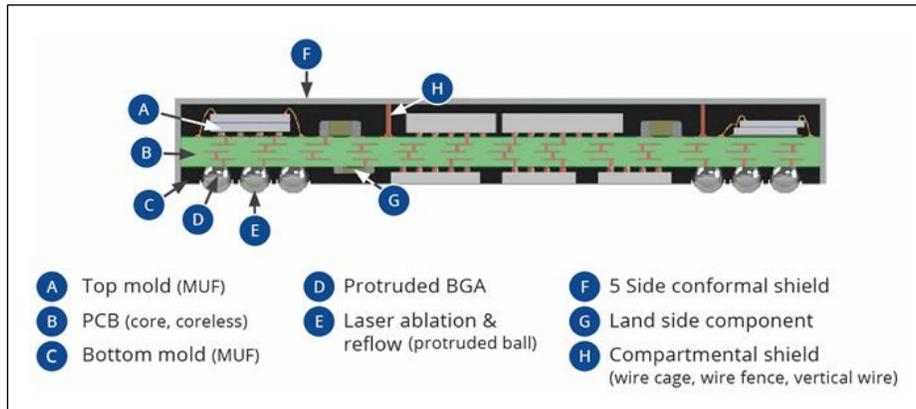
DSMBGA(Double-Sided Molded Ball Grid Array) 패키지
